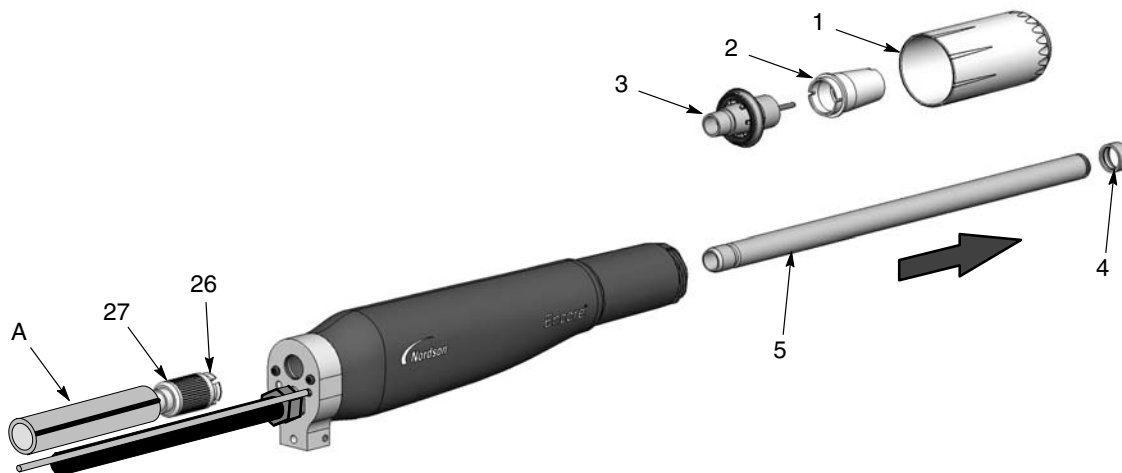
Mantenimiento - Pistola de montaje en barra mostrada sin montaje de pivote
